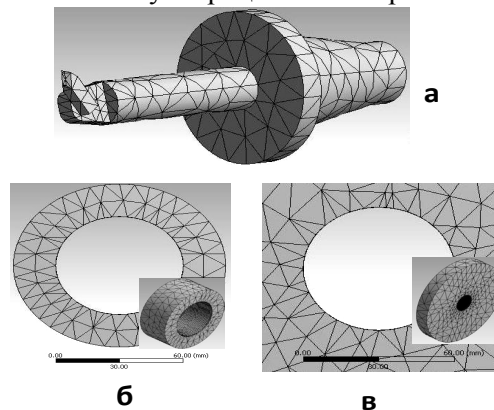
Моделі інструмента та деталей з отворами, що розточуються: а — борштанга; б — втулка; в — корпусна деталь
